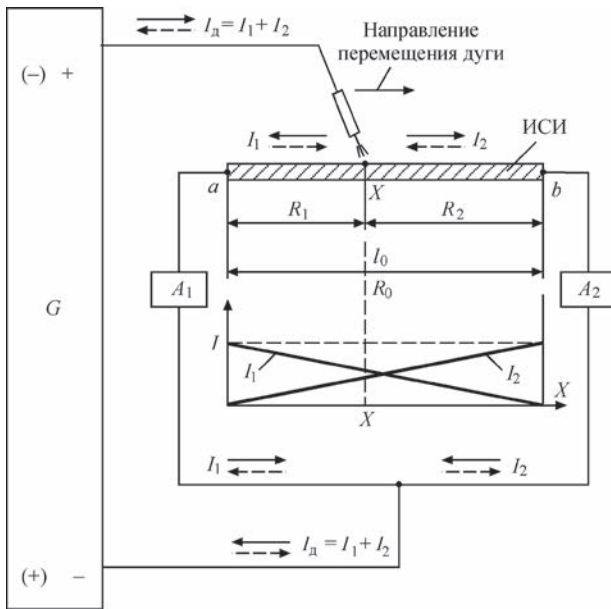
Схема резистометрического способа определения координаты пятна сварочной дуги и измерения скорости сварки в ТСС (описание см. в тексте; A_1, A_2 — датчики тока в ветвях sax и cbx сварочного контура)
